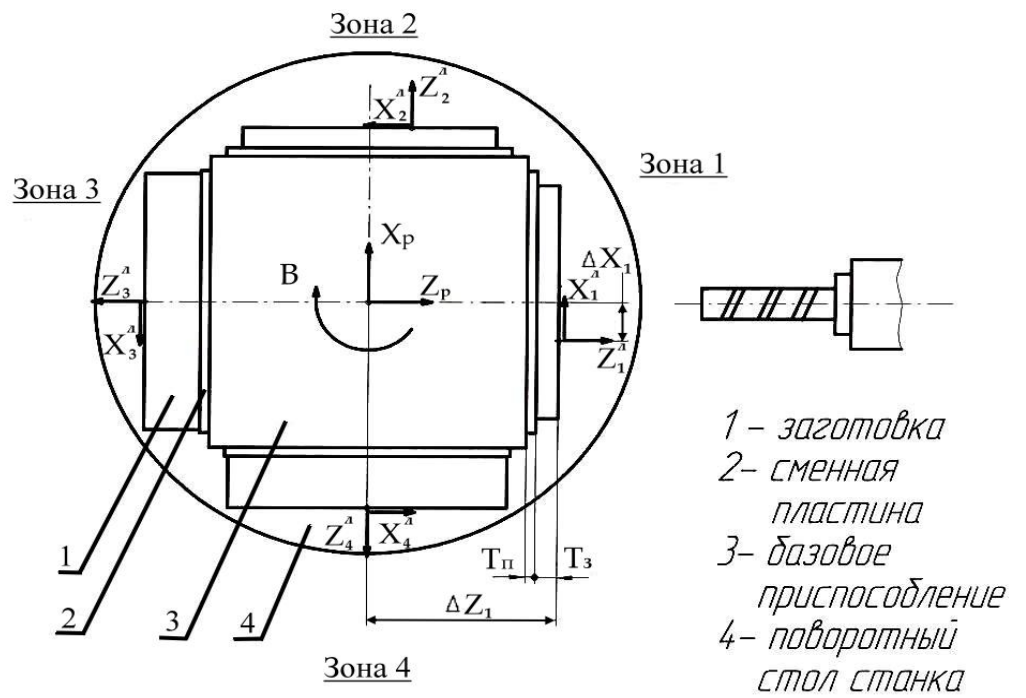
Схема установки заготовок в рабочей зоне станка
